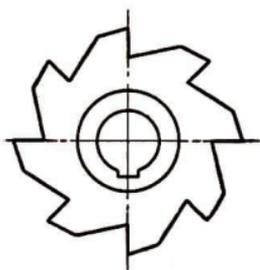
Fräser mit gefrästen Zähnen (spitzverzahnt)
